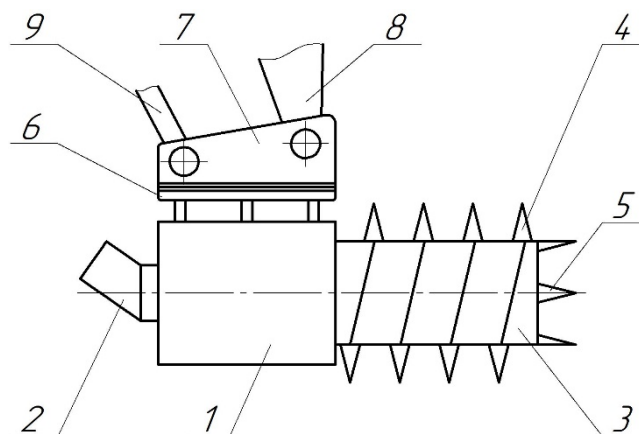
Принципова схема змінної фрезерної голівки до екскаватора ЭО-5123: 1 – корпус; 2 – гідромотор; 3 – фрези; 4, 5 – бокові та торцеві
